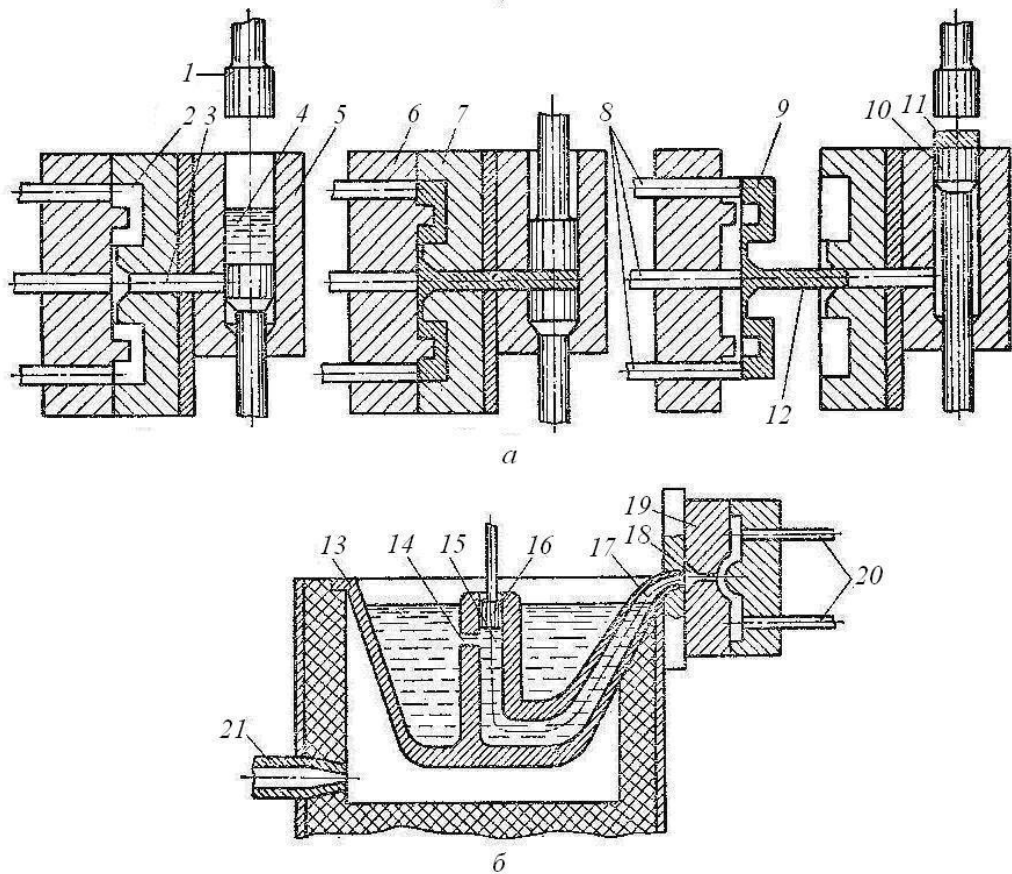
Схеми роботи поршневої машини: *а* – з холодною камерою: 1-поршень; 2, 6, 7-прес-форма; 3-ливниковий канал; 4-розплав; 5-камера тиску; 8-штовхачі; 9-виливок; 10-нижній поршень; 11,12-залишок розплаву; *б* – з гарячою камерою: 13-тигель; 14-отвір; 15-поршень; 16-камера тиску; 17-канал подачі розплаву у прес-форму; 18; 19-нижня частина пресформи; 20-штовхачі
